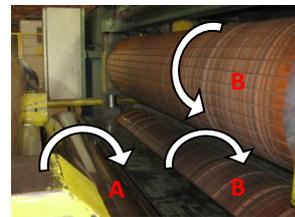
particolare rulli (A "billy roll" - B "pinch roll")
